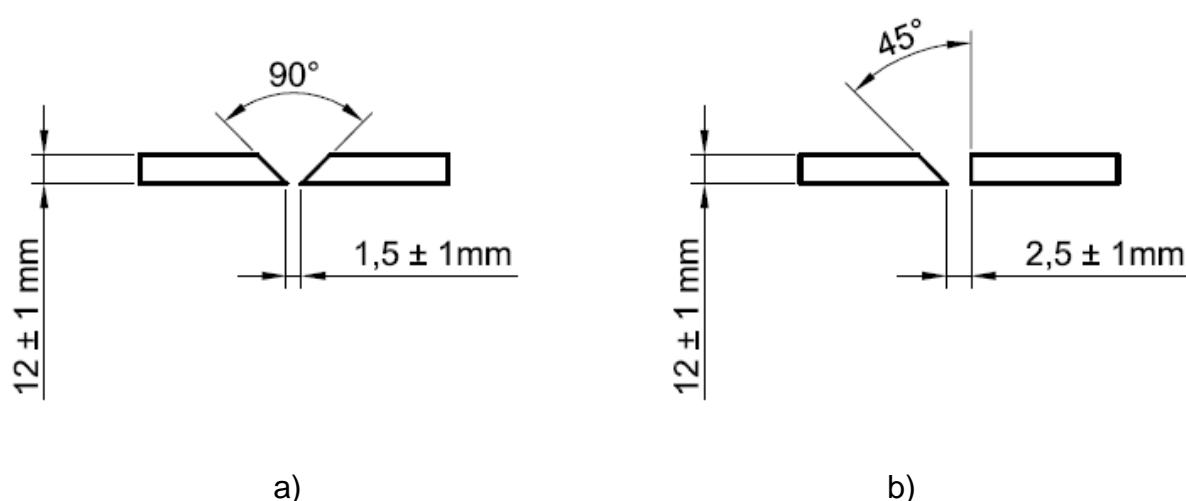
Dimensões e geometria do chanfro utilizadas no processo de soldagem GMAW em corpos de prova para ensaio de fadiga, evidenciando chanfro 1V (a) e $\frac{1}{2}V$ (b). Fonte: Autor
